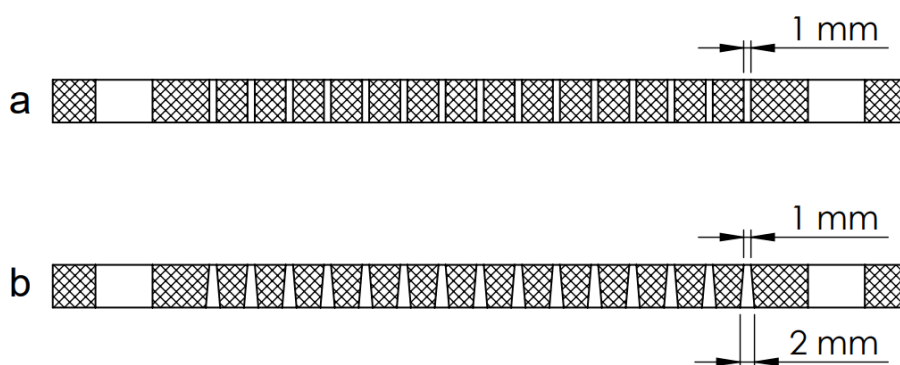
Dreno: a) seção reta e b) seção trapezoidal.
